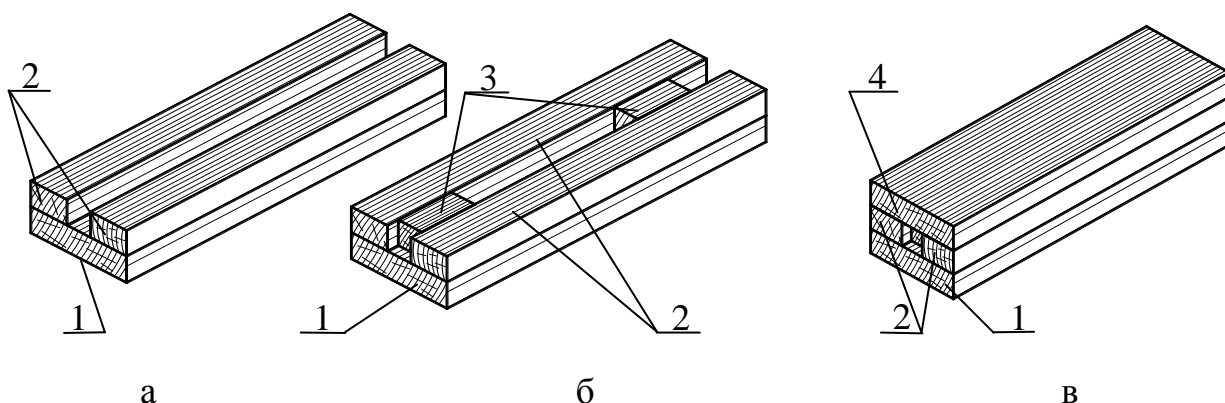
Етапи формування пакету для виготовлення порожнистого клеєного бруса: а – розміщення заготовок середнього шару; б – встановлення дистанційних брусків; в – встановлення заготовок верхнього шару;
